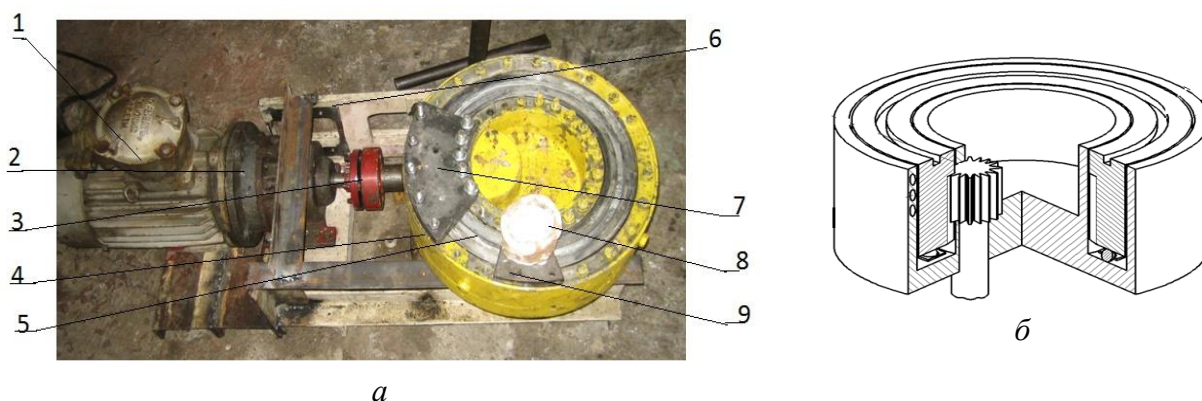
Установка непрерывного литья-прессования: *а* - общий вид;
